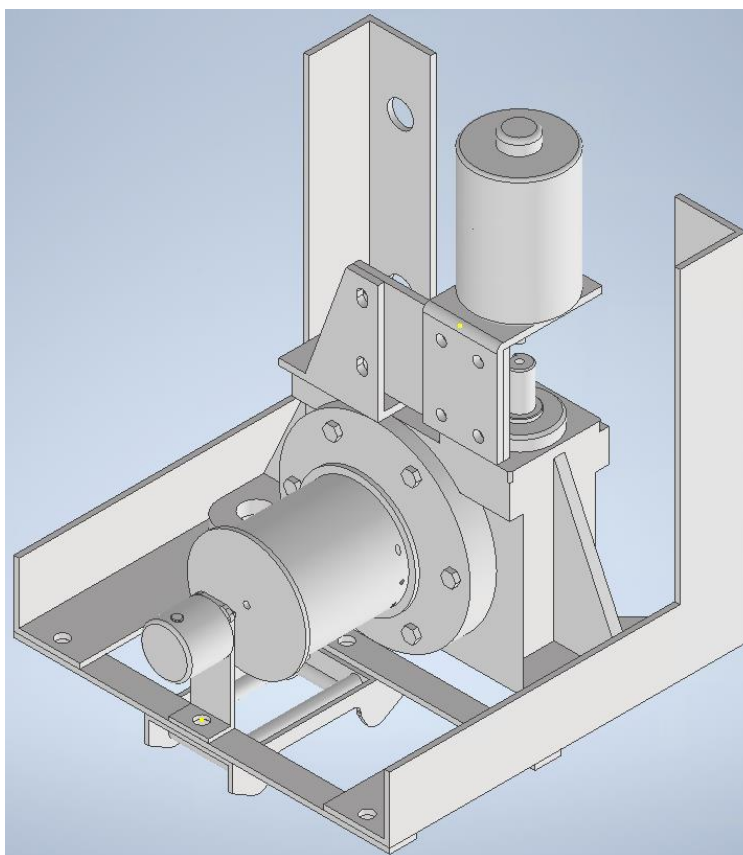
3D-модель сборки приводного модуля стенда
